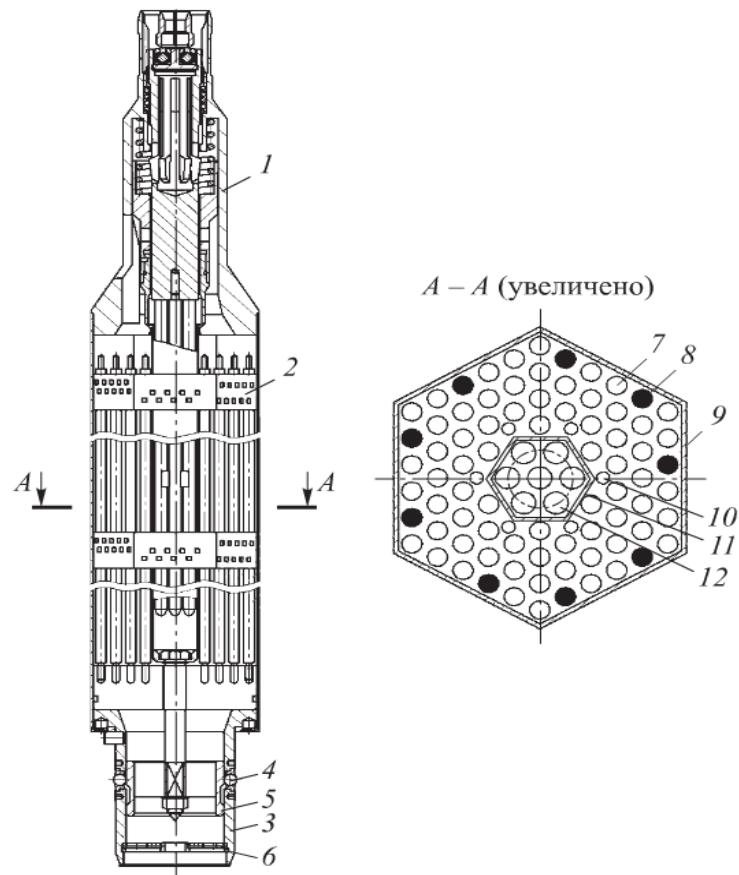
Общий вид ТВС реакторной установки РИТМ-200 [3]:
